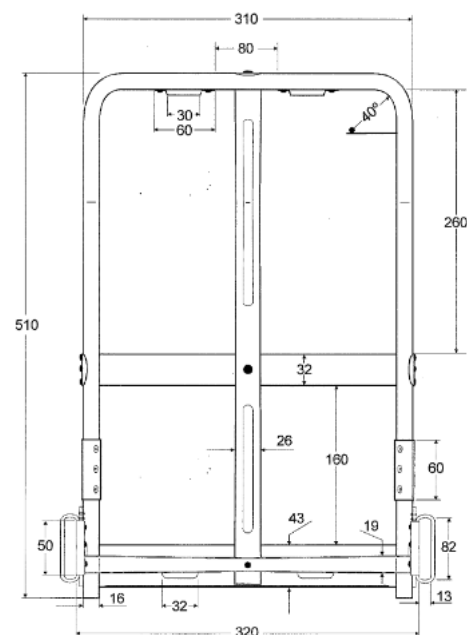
Vista frontal do suporte metálico (medidas em mm)
